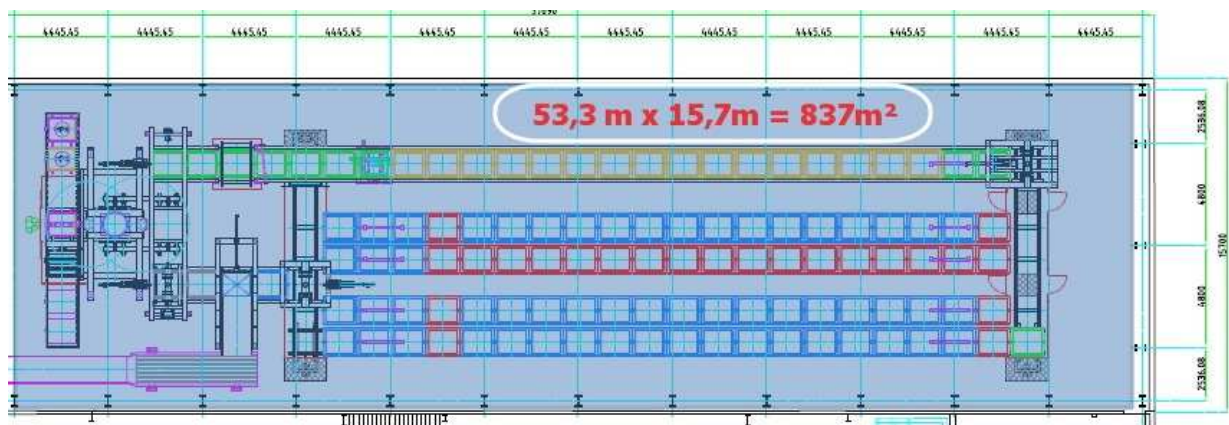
Layout einer Anlage in konventioneller Bauweise
